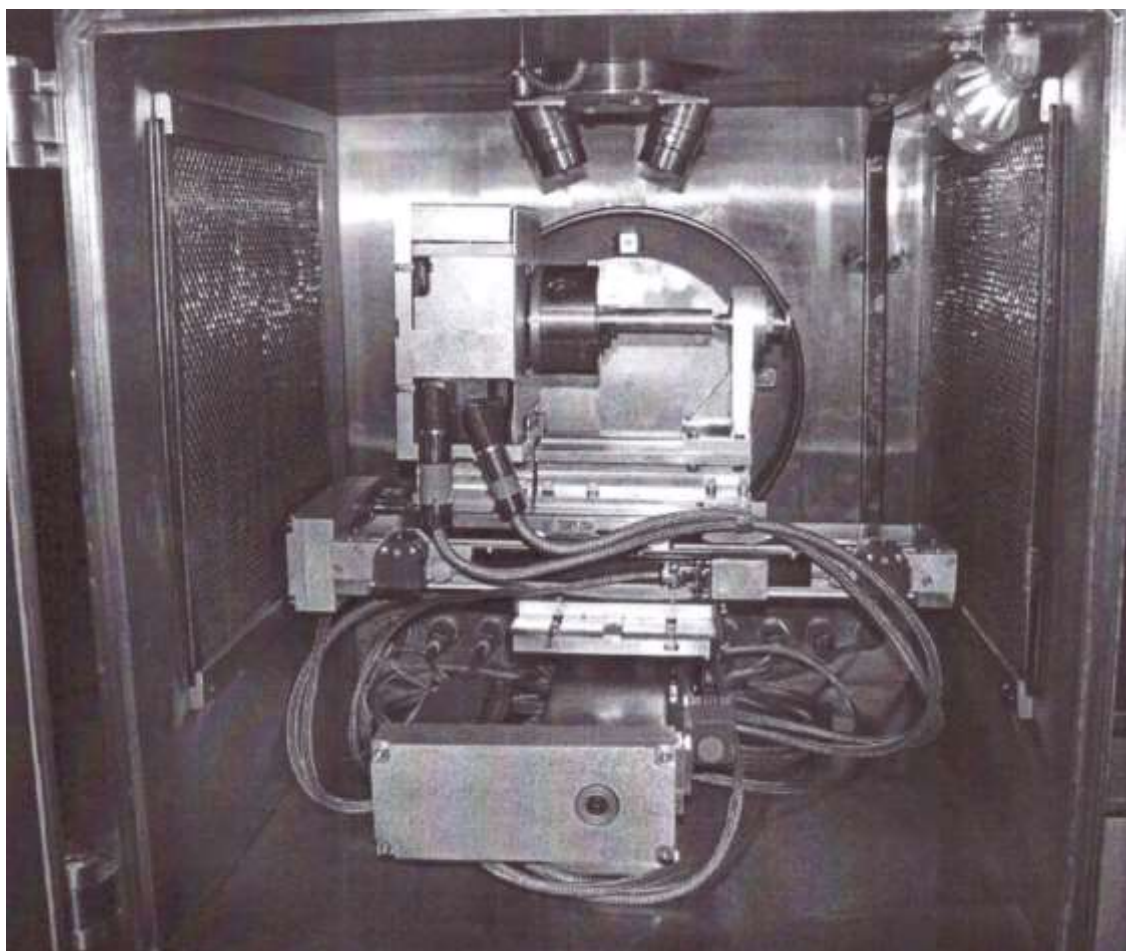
Двохкоординатний робочий стіл з установленими на ньому універсальним обертальним столом і задньою бабкою.
